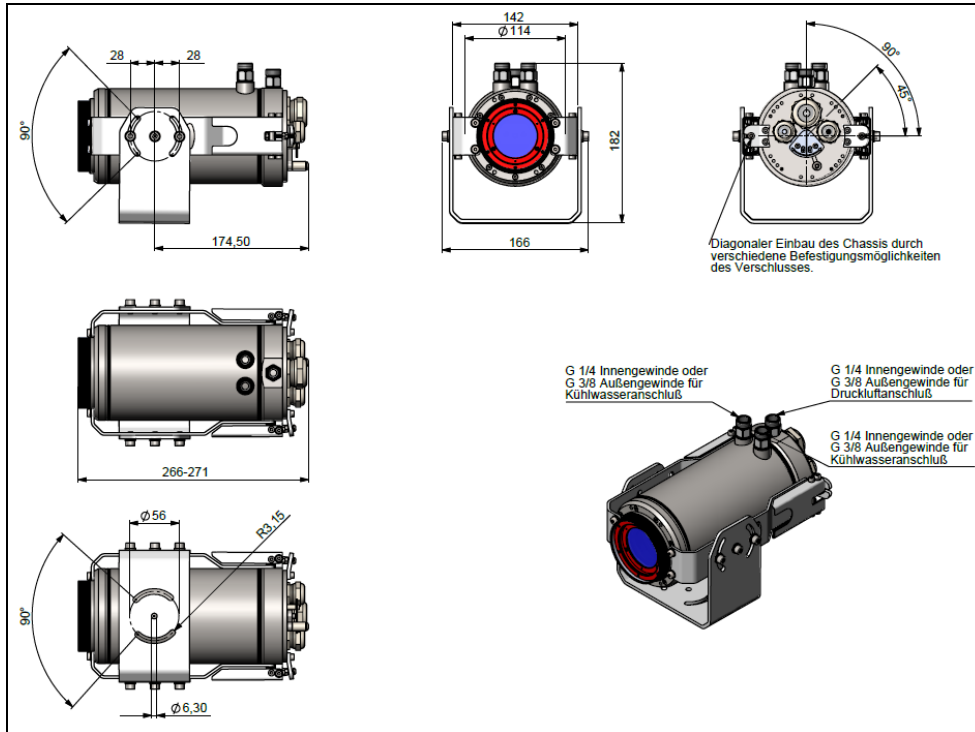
Cooling Jacket Advanced, Standard-Version – Komplettansicht
